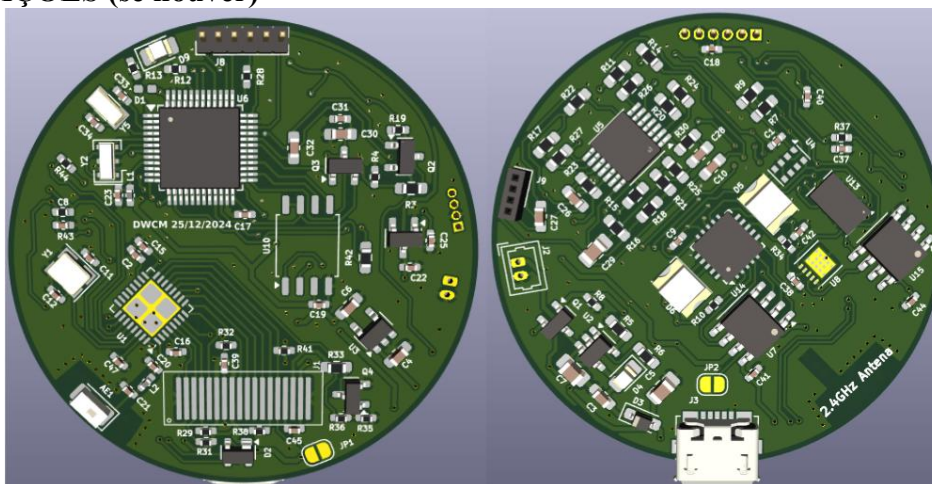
Layout original da PCB para o eGluco (ambas as camadas).
